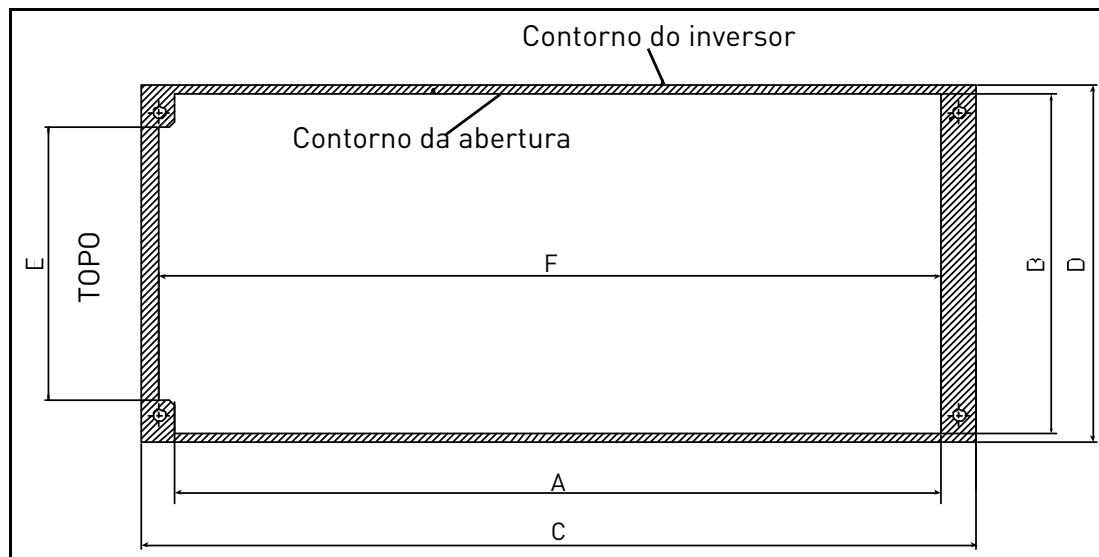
Dimensões do recorte para montagem com flange do MR4 ao MR6
